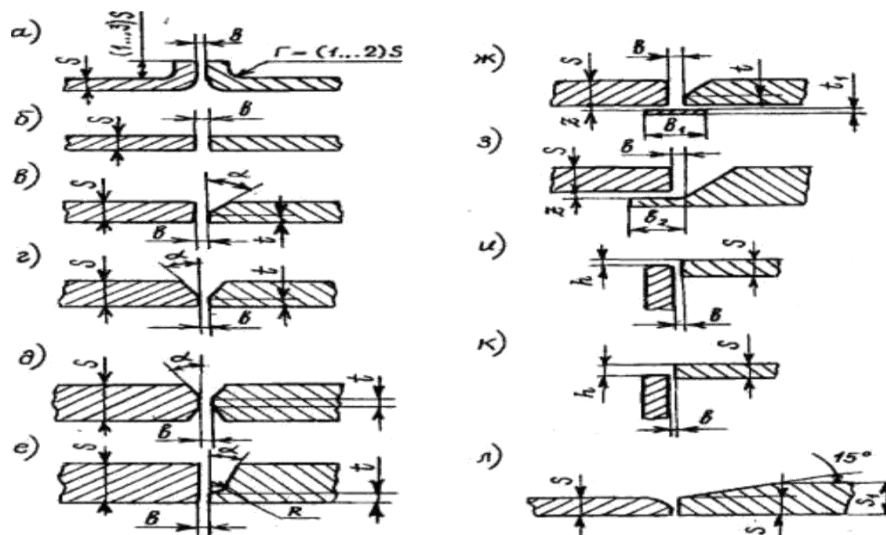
Виды подготовки кромок под сварку
